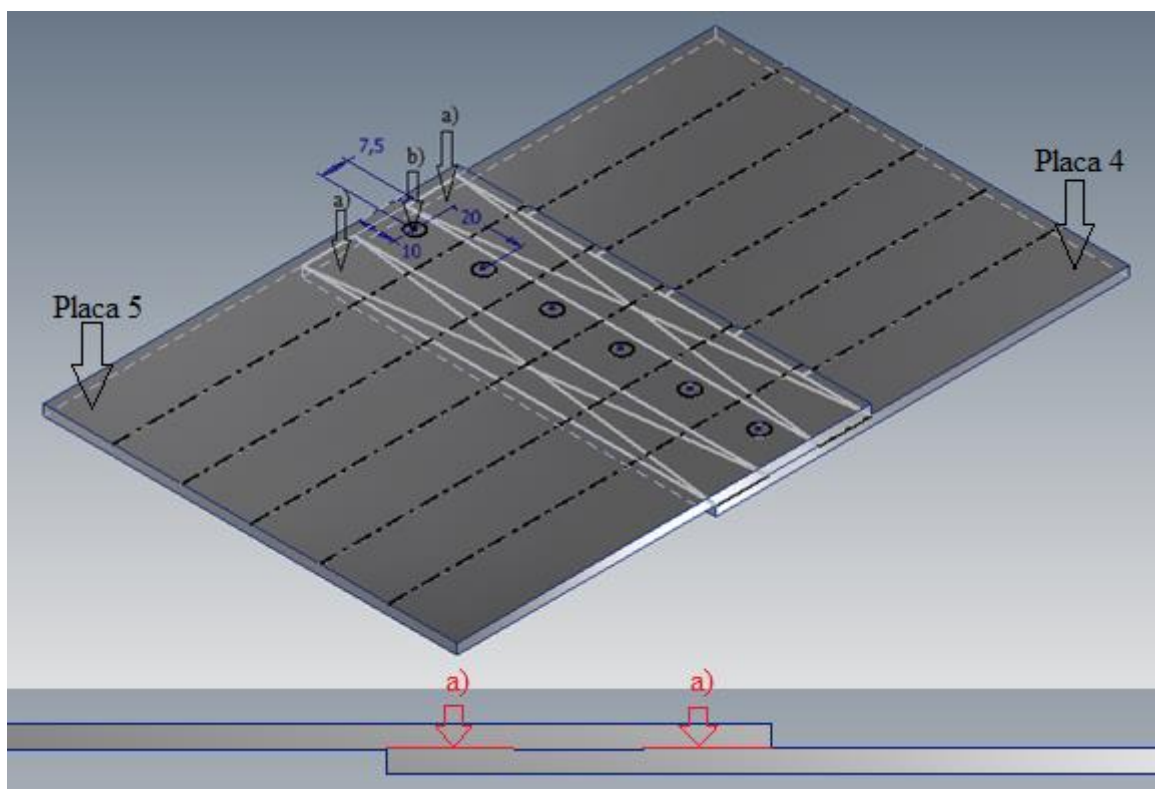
a) Locais de aplicação do adesivo e b) pontos de soldadura para os provetes da série 2.
